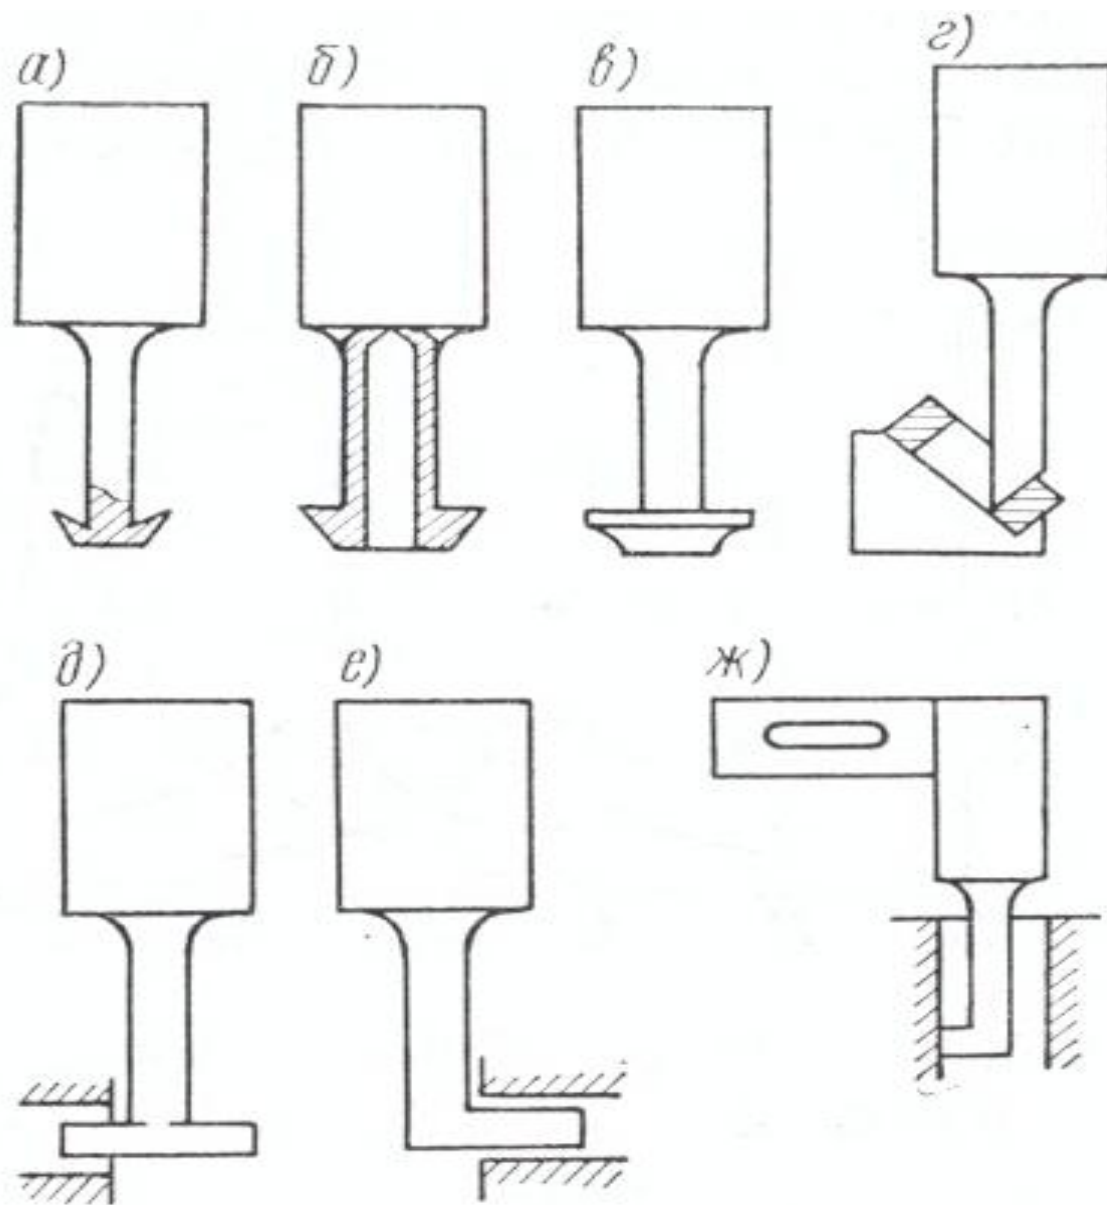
Инструменты для обработки глухих отверстий и наружных поверхностей
